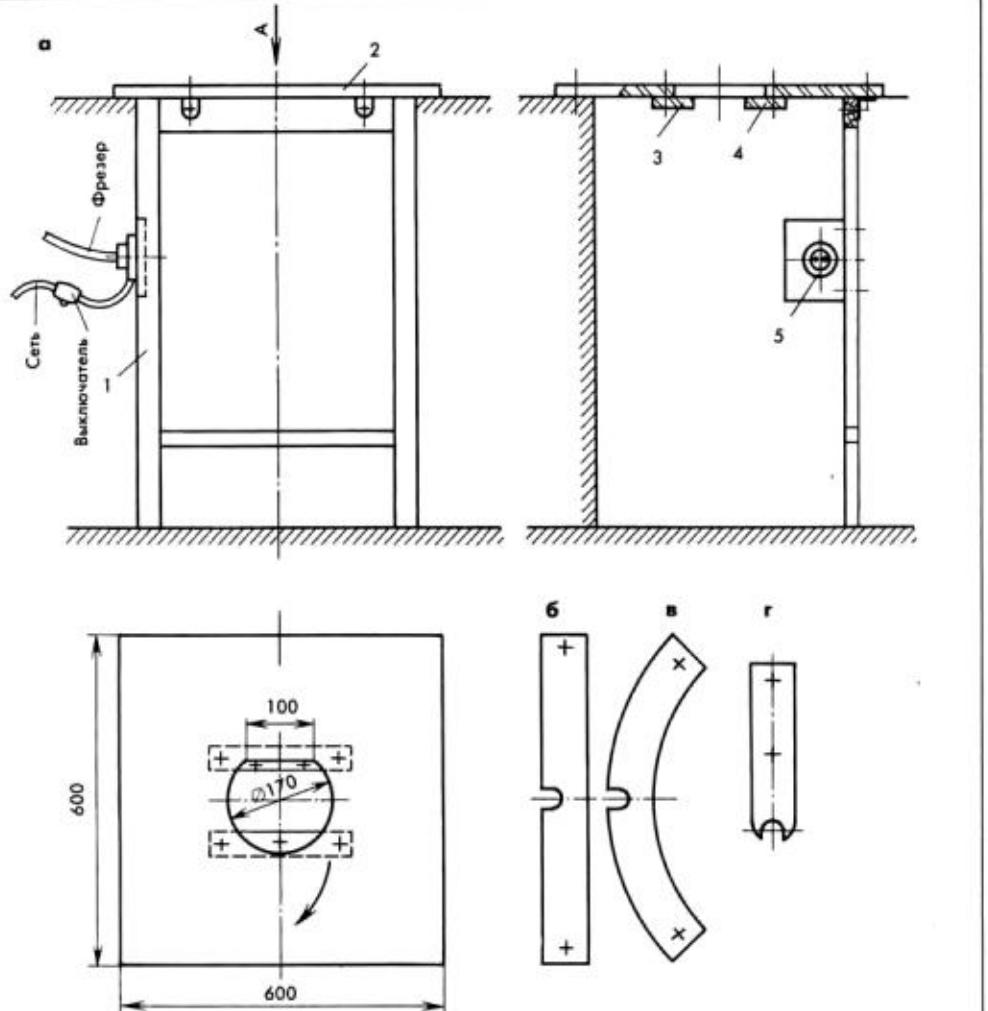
Стол для фрезерования с нижним расположением шпинделя и направляющие линейки для фрезерования:
